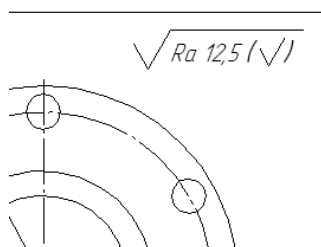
Обозначение неуказанной шероховатости поверхности
